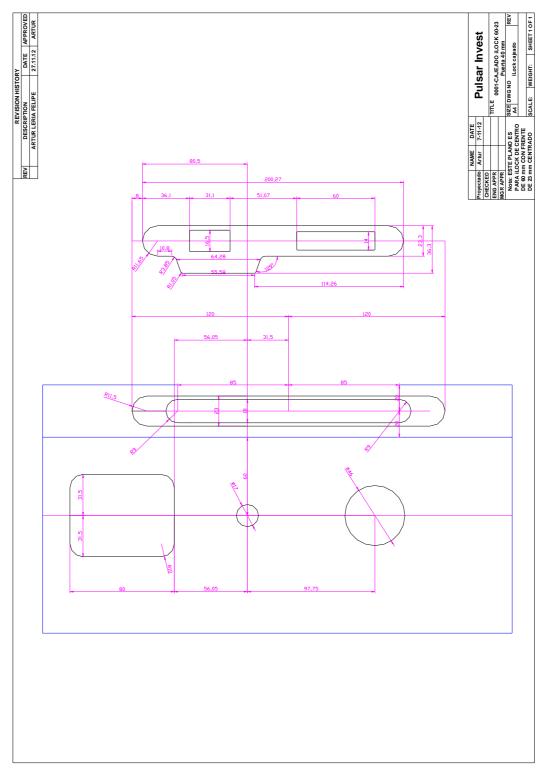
Cajeado de la cerradura iLock para una puerta de 40 mm de grueso.
